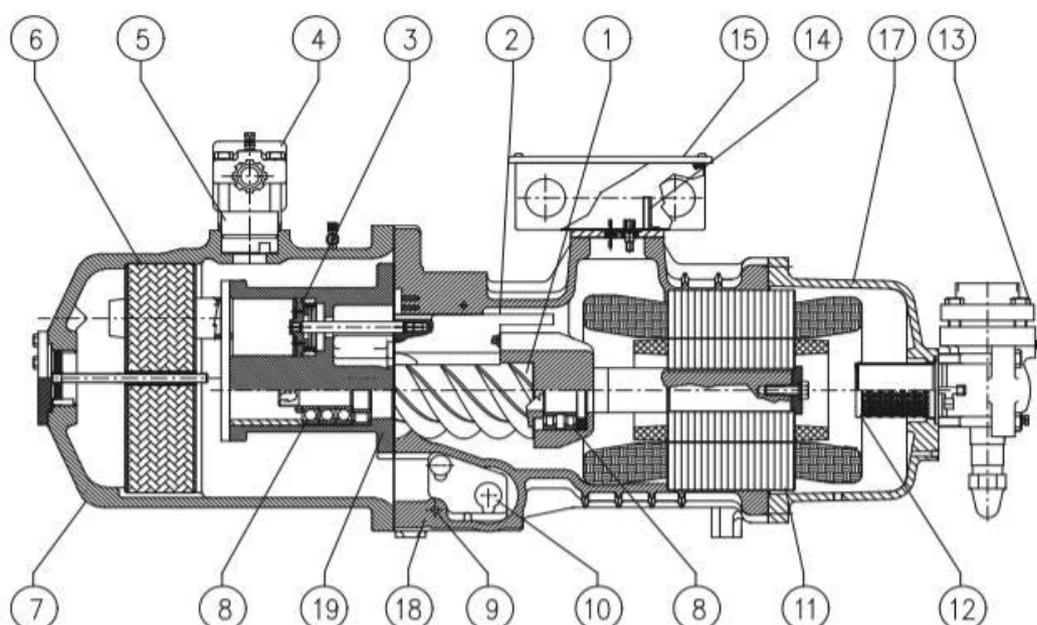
Основные узлы компрессора 1 - роторы; 2 - слайд клапан; 3 - поршня управления клапаном; 4 - разгрузочный клапан запорный; 5 - обратный клапан; 6 - маслоотделитель; 7 - сепаратор; 8 - подшипники качения; 9 - подогреватель картера; 10 - масляный фильтр; 11 - электродвигатель; 12 - всасывающий фильтр; 13 - всасывающий клапан; 14 - устройство защиты; 15 - электрическая коробка; 16 - крышка всасывания; 17 - корпус; 18 - опора.
